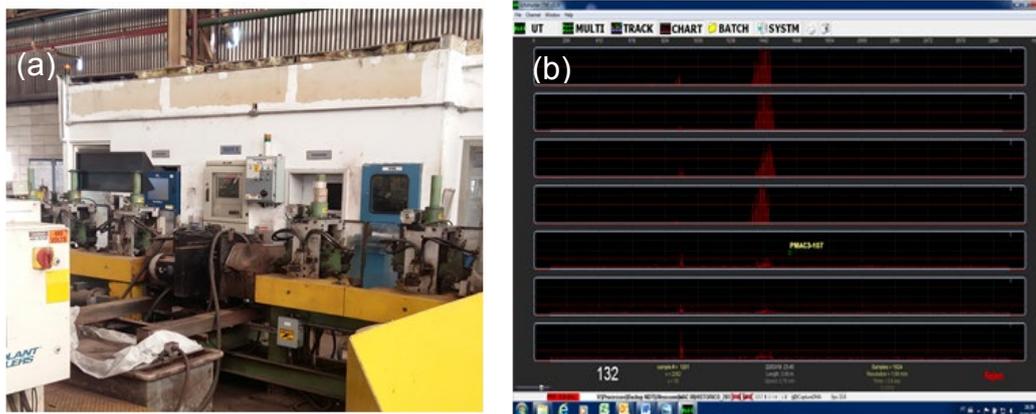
(a) imagem do equipamento de inspeção por ultrassom (b) exemplo da tela de registro da inspeção.
